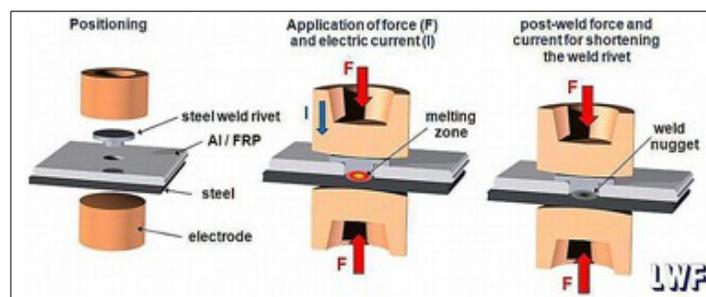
soudage par résistance avec élément (source: Laboratory of Materials and Joining Technology, l'université de Paderborn)
